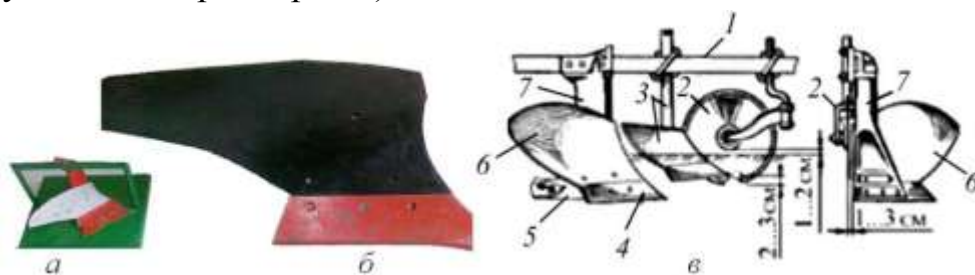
Плуг лемешный навесной ПН-40: *а* – макет корпуса; *б* – натурный образец; *в* – схема устройства: 1 – рама; 2 – дисковый нож, 3 – предплужник; 4 – лемех основного корпуса плуга, 5 – полевая доска; 6 – отвал; 7 – стойка корпуса
